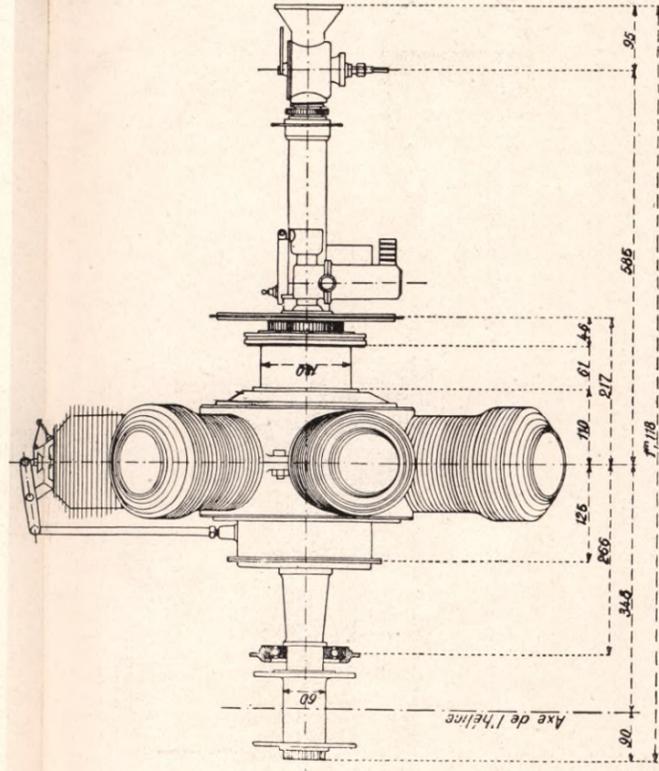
60 P 7-Zylindermotor, Raumzeichnung, Seitenansicht.
